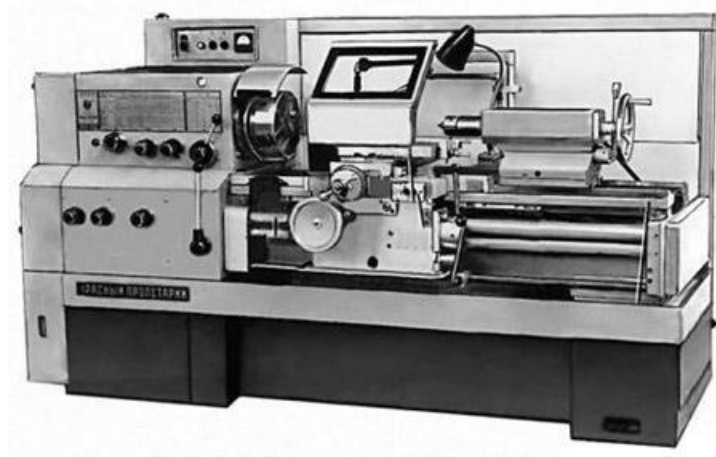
Токарно-гвинторізний верстат 16К20
